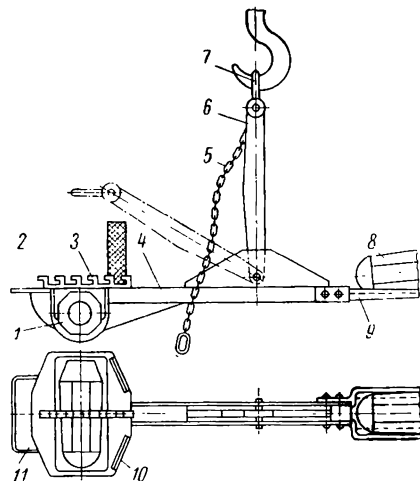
Схема устройства посадочной вилки: 1 — сменный груз; 2 — полость для размещения груза; 3 — гребенка; 4 — двутавровый стержень; 5 — цепь; 6 — рычаг; 7 — рым; 8 — слиток; 9 — вилка; 10 — экран; 11 — ручка
